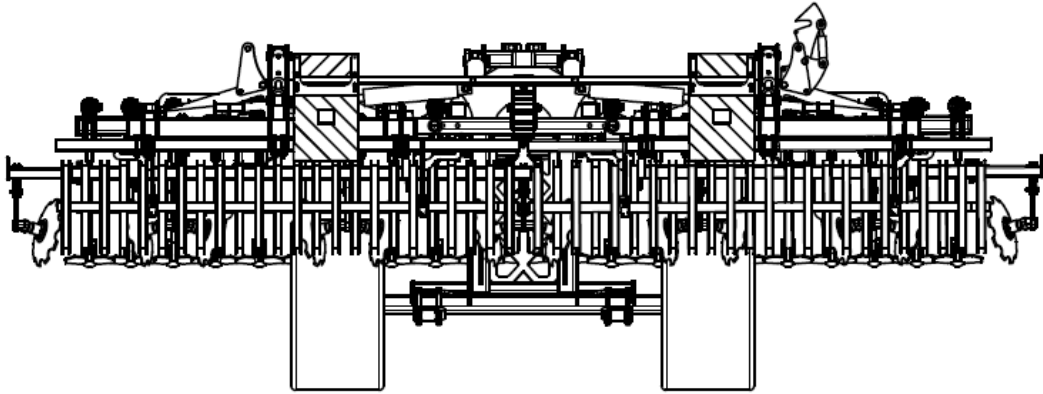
Vue de la machine à la fin de la séquence d'ouverture des ailes. Les bras de la machine sont complètement ouverts.
